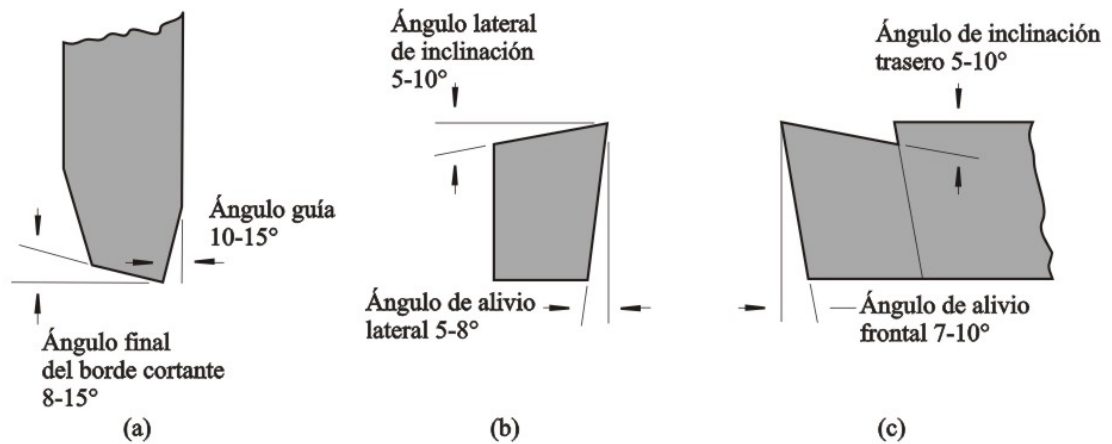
Geometrías sugeridas para herramientas de corte de punta única en el torneado del acero inoxidable. (a) Vista inferior. (b) Vista frontal. (c) Vista lateral.
